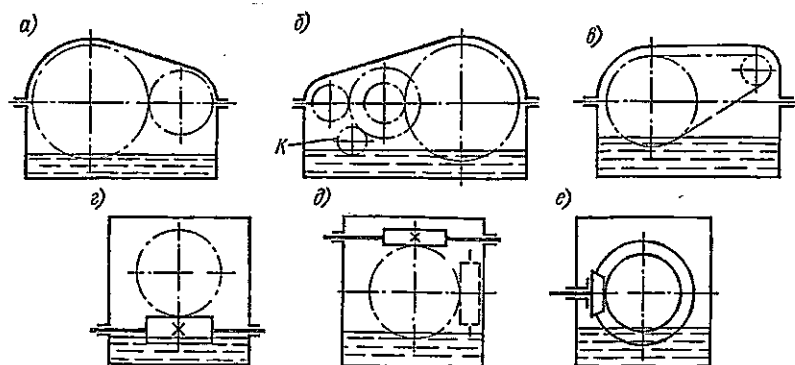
Смазывание погружением (картерное смазывание): а — цилиндрическая зубчатая передача; б — цилиндрическая зубчатая передача со вспомогательным смазывающим колесом; в — цепная передача; г, д — червячная передача; е — коническая зубчатая передача
